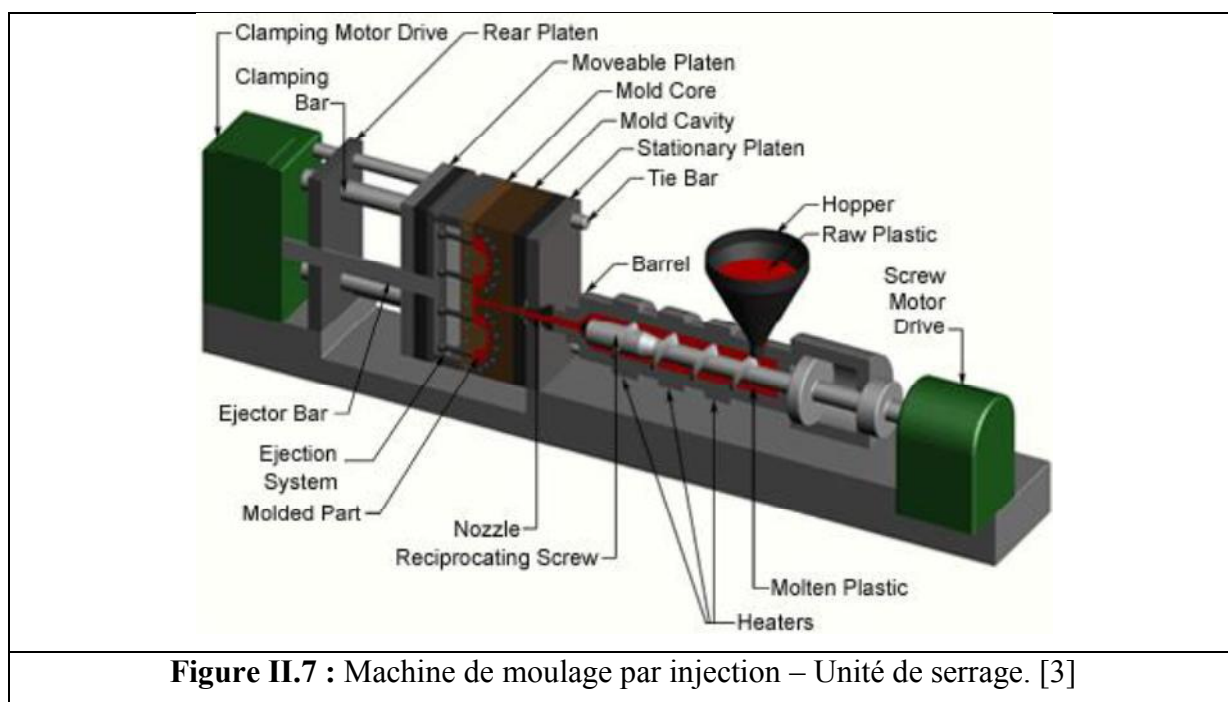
Machine de moulage par injection – Unité de serrage. [3]
